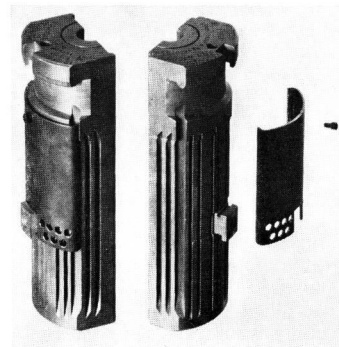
Fertigform zur Verwendung mit Fertigformenhaltern mit innerer Kühlung, mit angeschraubten und abgenommenen Kühlblechen.
